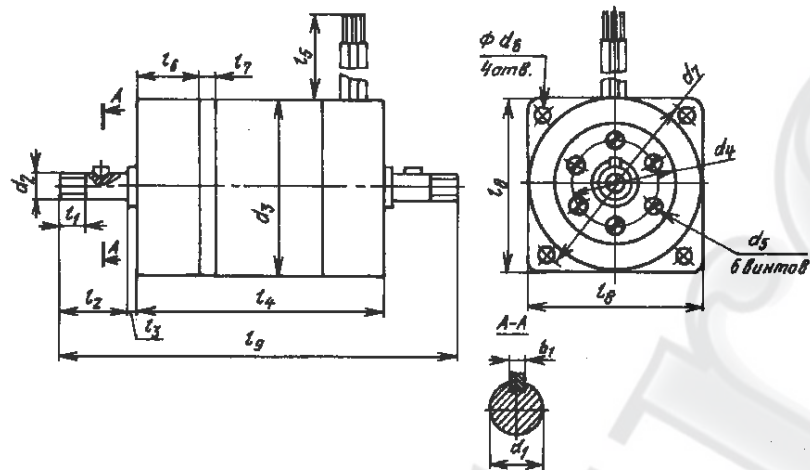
Габаритные и присоединительные размеры двигателей (исполнение фланцевое с двумя свободными концами вала)
